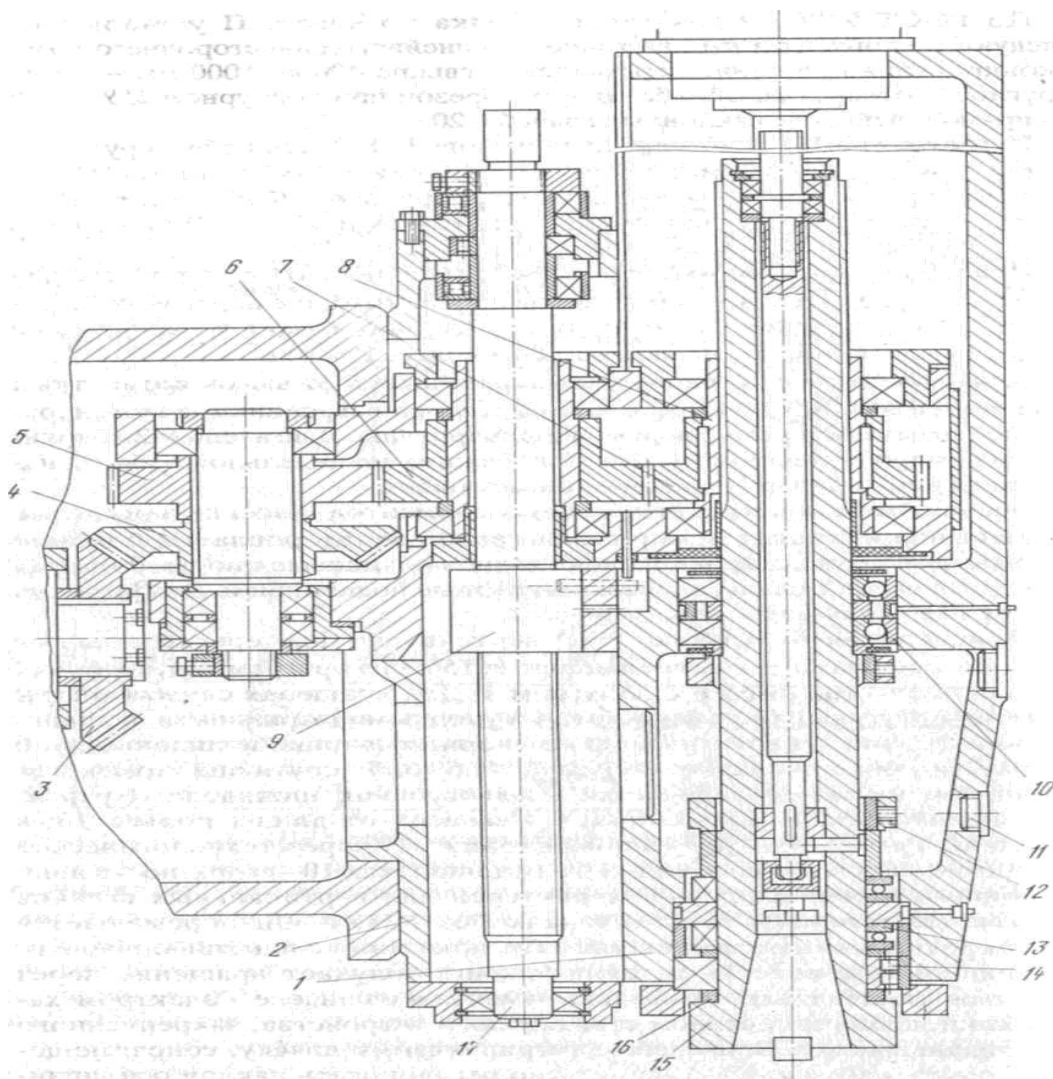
Шпиндельная бабка с ползуном вертикально-фрезерного станка с ЧПУ.
